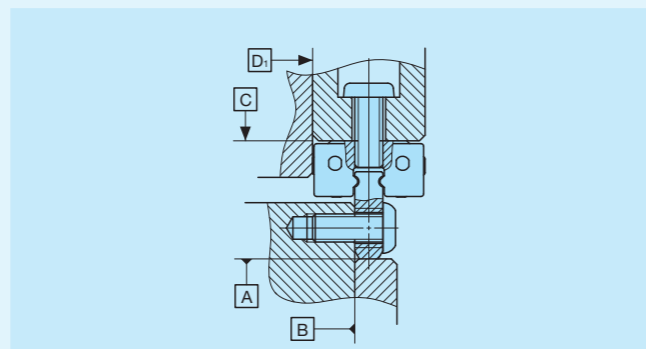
Superfície de montagem de referência de LWL1...Y e estrutura de montagem típica ②
